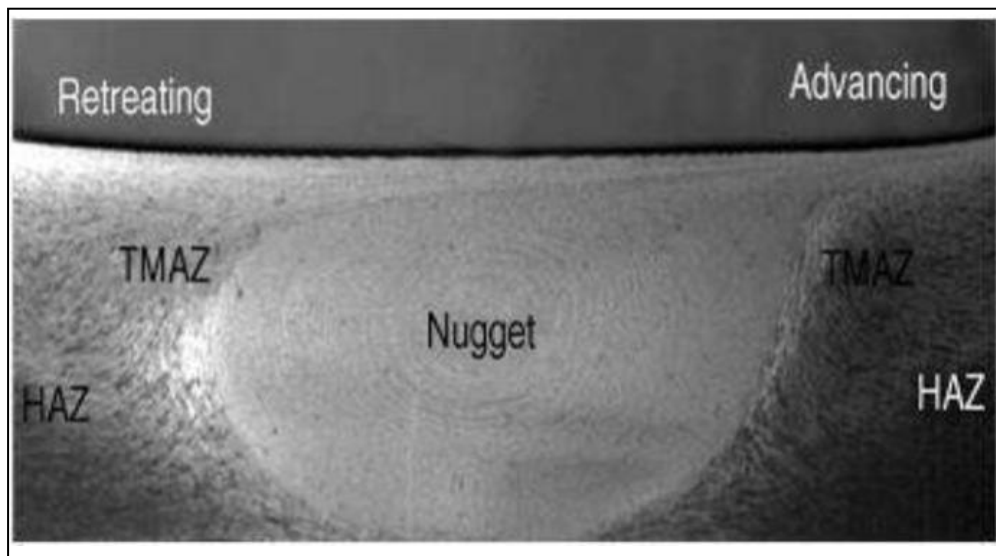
Section d'une soudure réalisée sur un alliage d'aluminium. [34]
